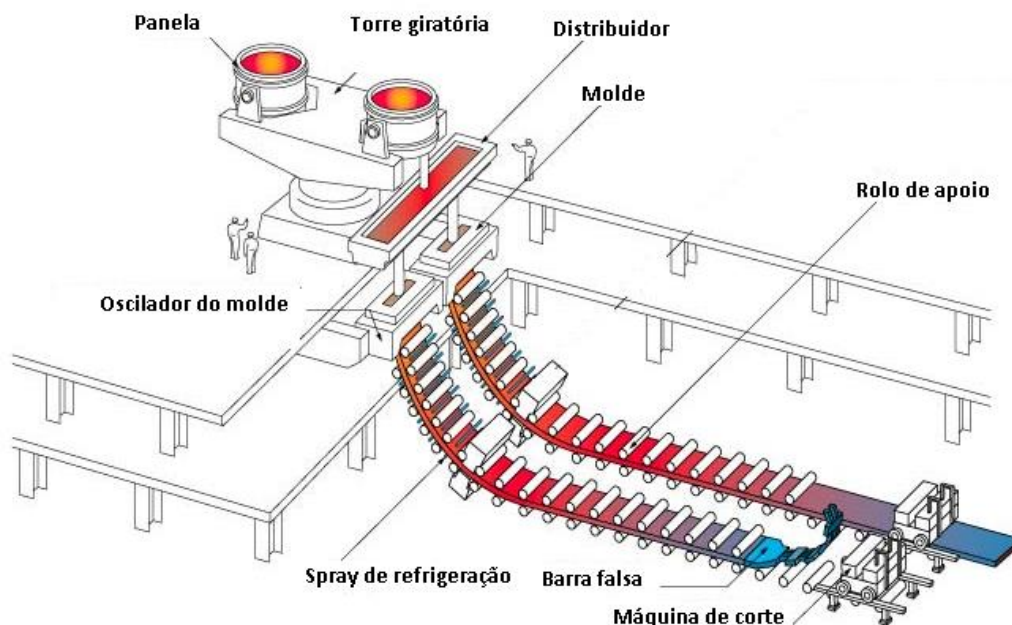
Desenho esquemático de máquina de lingotamento contínuo de placas.
